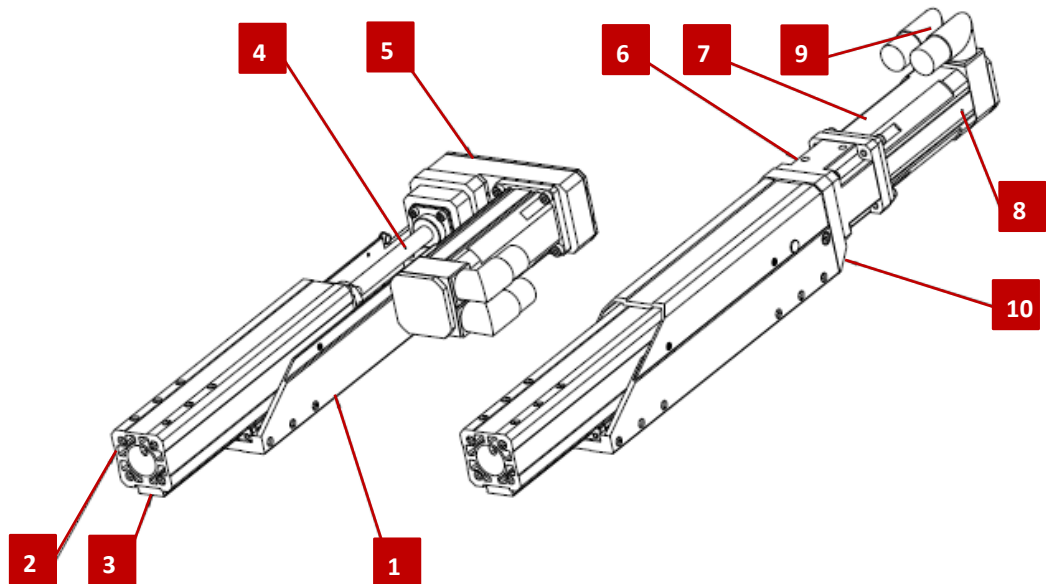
Aufbau des Spindelauslegers (exemplarisch)
